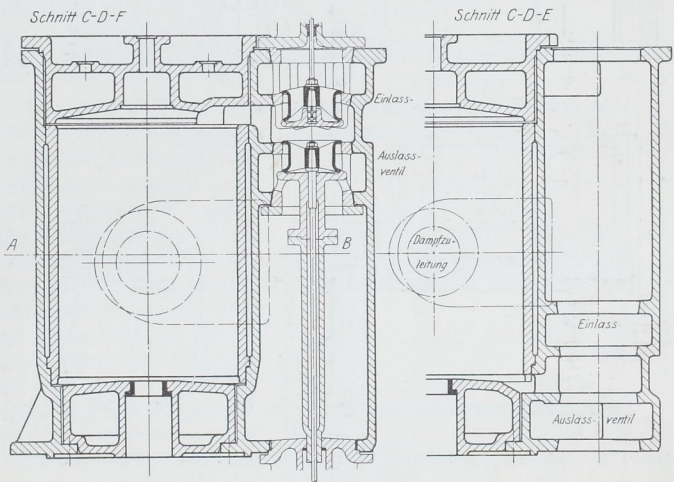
Zylinder mit Ventilsteuerung für stehende Maschinen.
